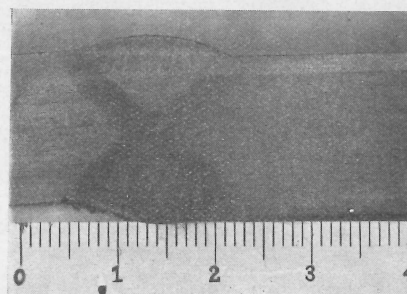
Coupe transversale dans la soudure représentée figure 8a.
